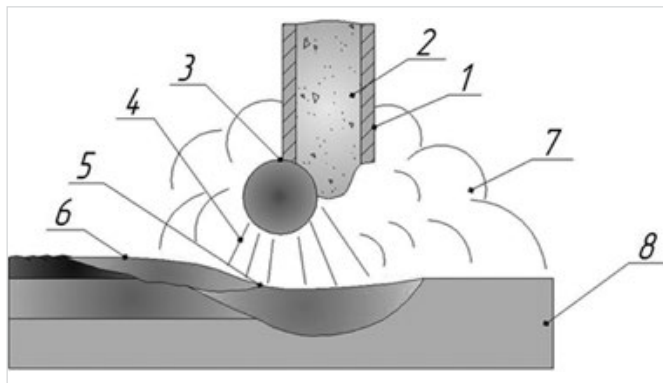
Схема процесса сварки самозащитной порошковой проволокой. 1 — стальная оболочка, 2 — порошковый сердечник, 3 — капля металла, 4 — электрическая дуга, 5 — сварочная ванна, 6 — шлак, 7 — образующийся защитный газ, 8 — свариваемая (наплавляемая) поверхность
